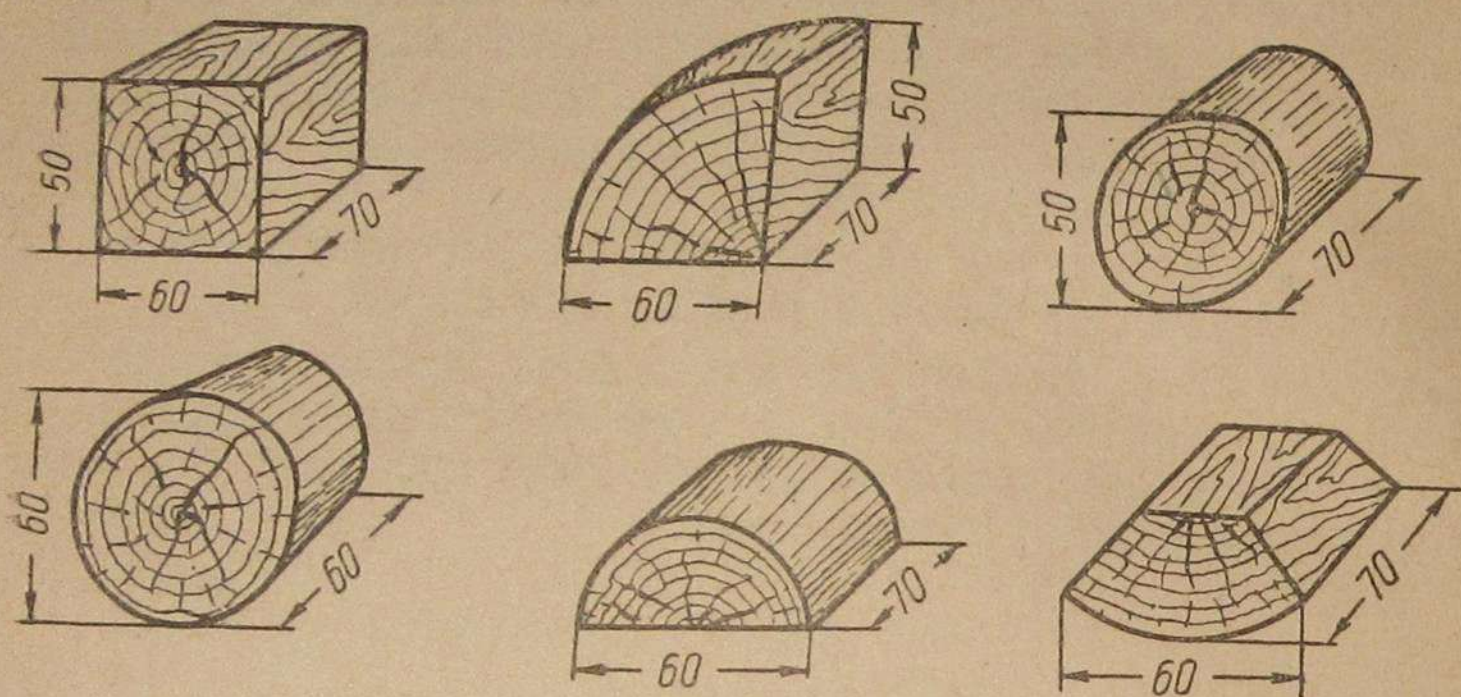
Образцы чурок для газогенераторов ЗИС-21
